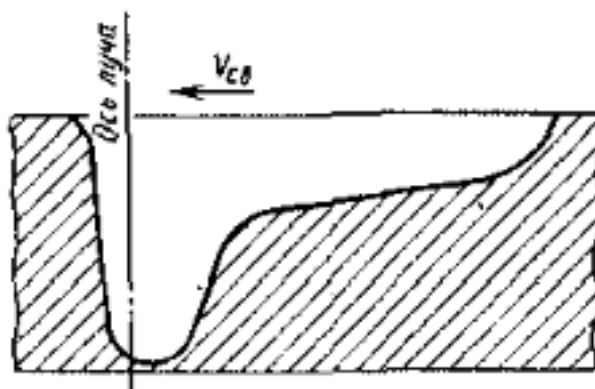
Продольное сечение сварочной ванны
